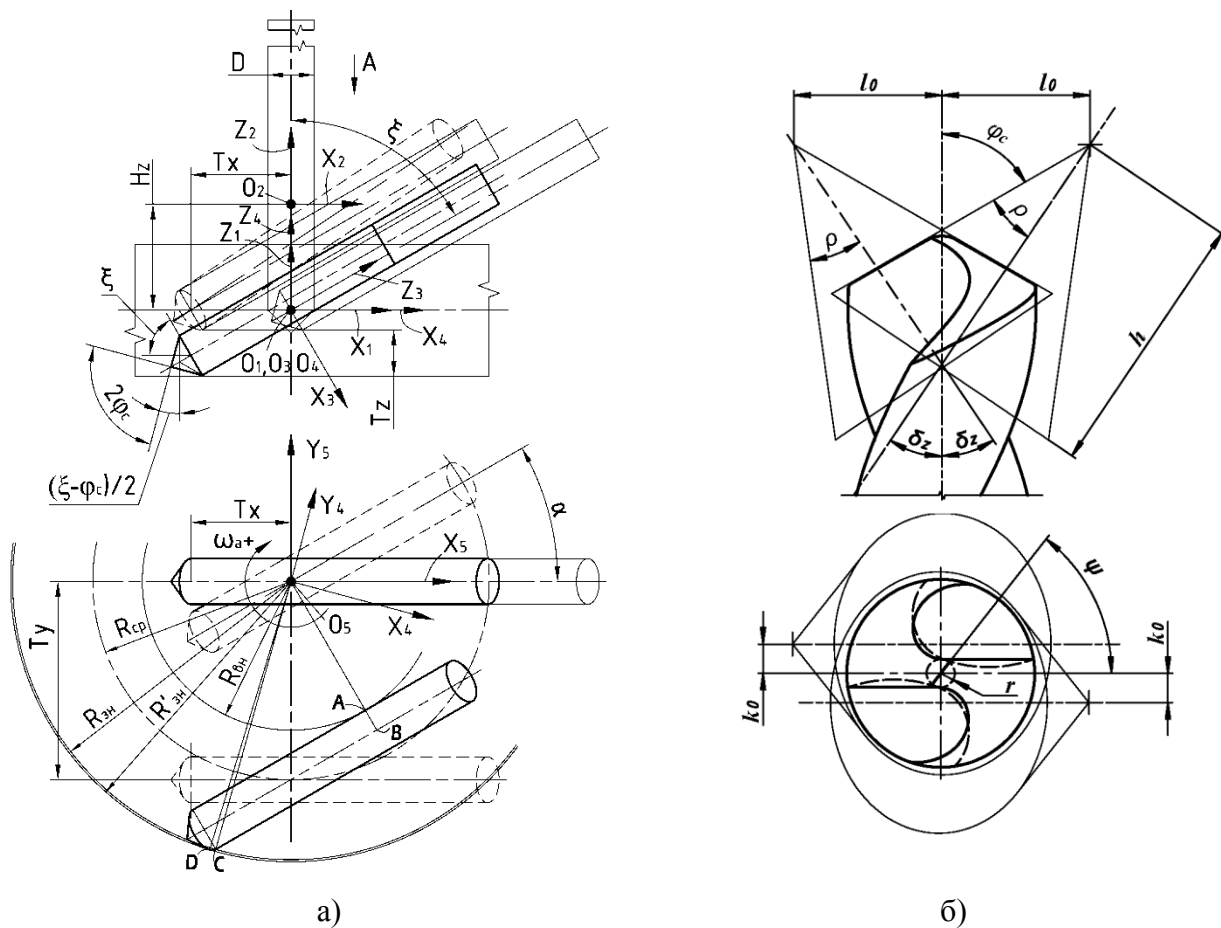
Схема установки свердла в робоче положення в роторному верстаті для обробки з круговою та азимутальною подачами Розрахункова схема задньої поверхні спірального свердла при заточці по конусу.
